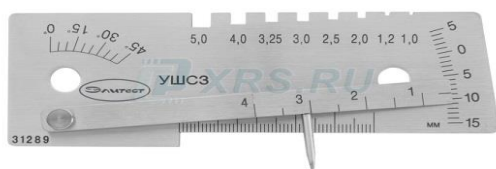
Универсальный шаблон сварщика УШС-3
